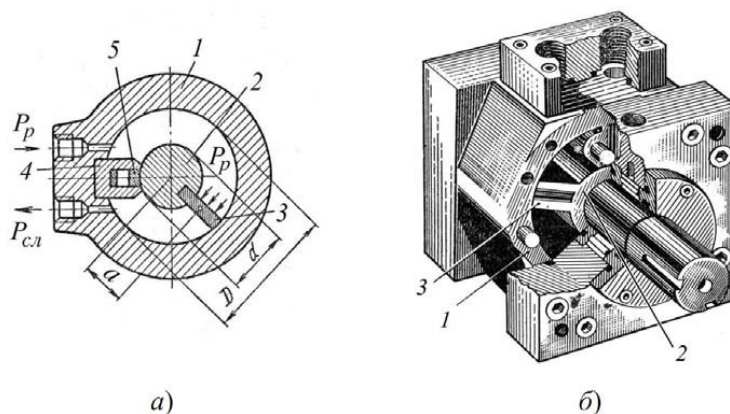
Поворотный однолопастной гидроцилиндр: а – схема; б – общий вид
